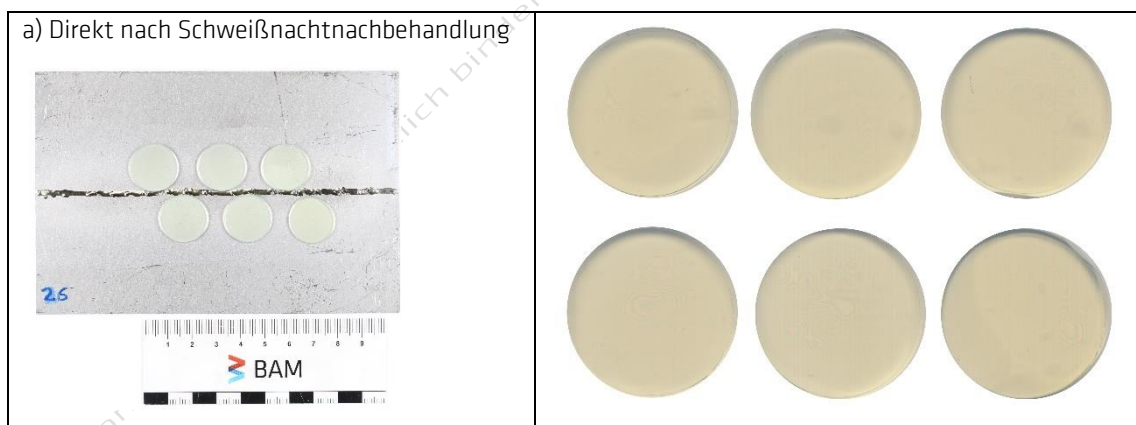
KorroPad® Prüfung auf Blechcoupon 26 (l.), 1.4404, 20 s Schweißnahtnachbearbeitung; Prüfergebnis nach 15 min (r.); KorroPads mit Anzeige blau gerahmt
